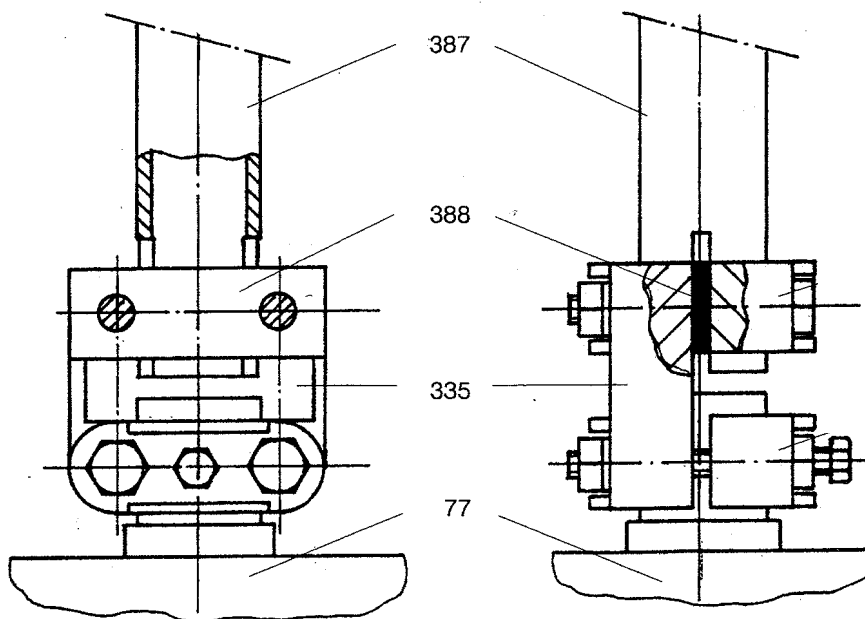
Установка приводного механизма разъединителя; раздельный монтаж при размере т3 от 6 до 12м. Монтажные размеры (Деталь А и деталь Б)
